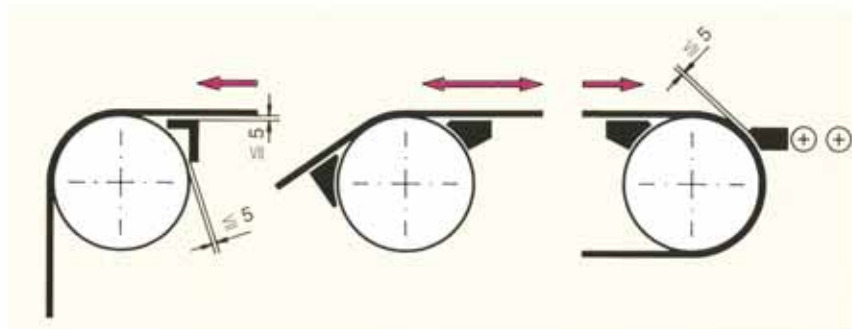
Barres de protection et cornières de protection placées aux zones d'engagement et d'entraînement.
